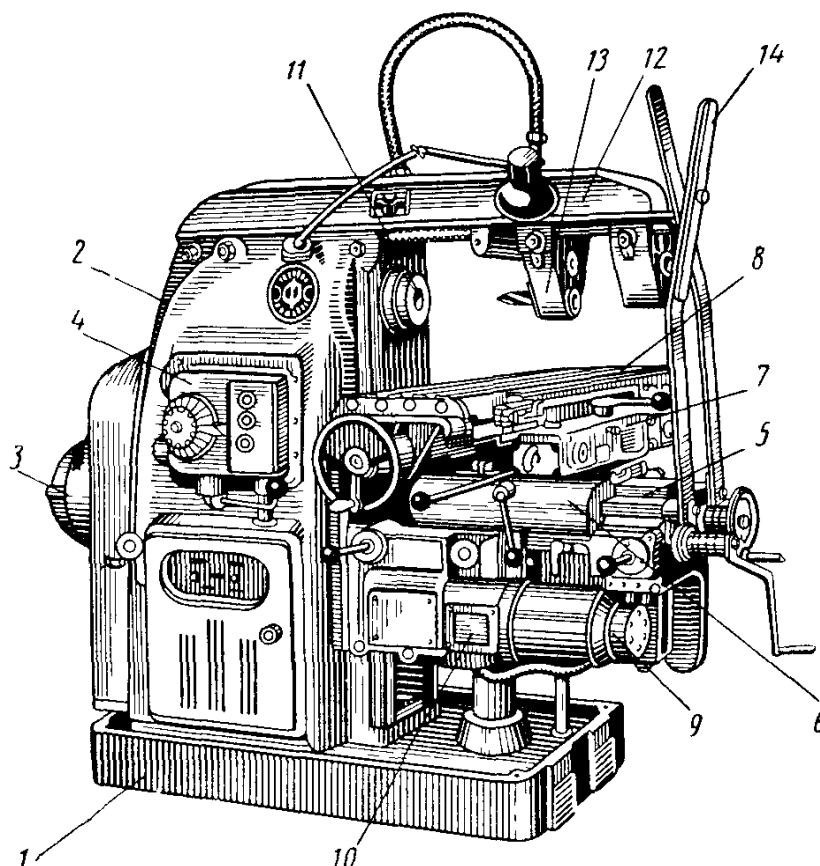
Універсальний горизонтально-фрезерний верстат
